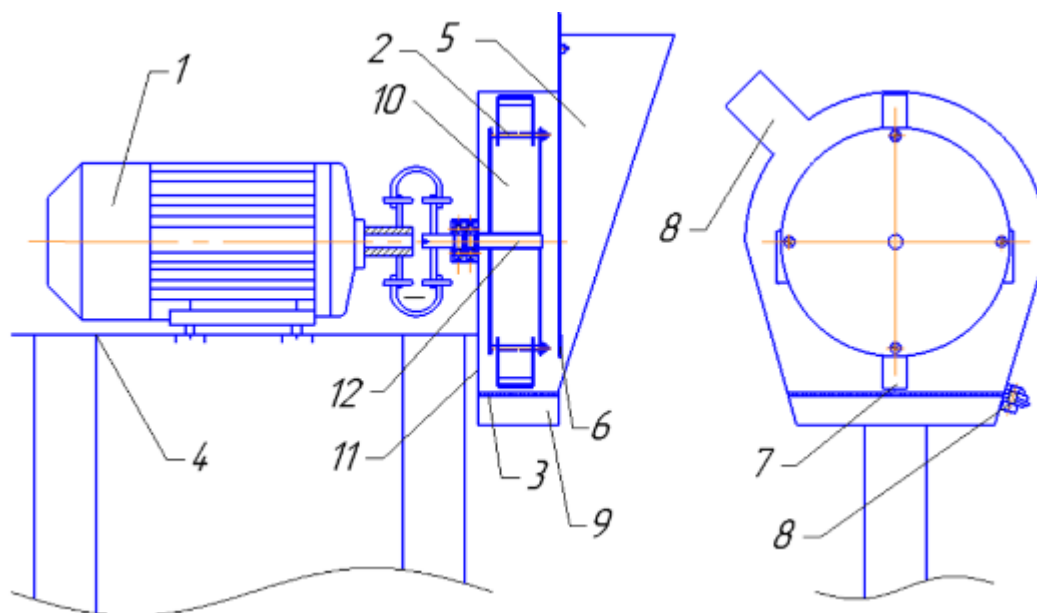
Загальний вигляд малогабаритного молоткового подрібнювача: 1 - електродвигун; 2 - палець; 3 – сито кормодробарки; 4 - стійка; 5 - бункер; 6 - заслінка; 7 - молоток; 8 – загрузочний отвір для качанів кукурудзи; 9 – зажим для сита; 10 – вивантажний отвір; 11 – подрібнююча камера; 12 - корпус; 13 – ротор
